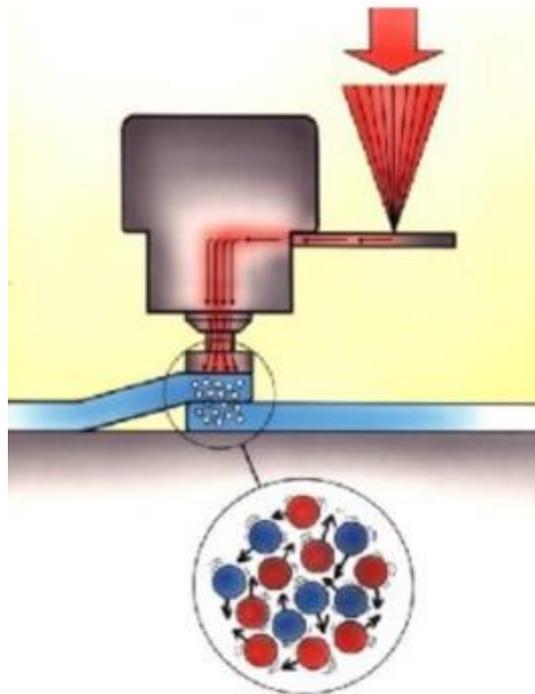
Esquema de soldadura por alta frecuencia. [3]
